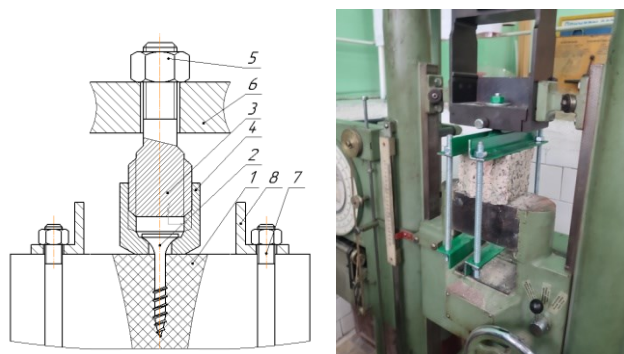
Оснастка. 1 – испытываемый образец, 2 – саморез или гвоздь, 3 – резьбовая вставка, 4 – колпачковая гайка, 5 – гайка, 6 – подвижная рамка прессы, 7 – шпилька, 8 – уголок
